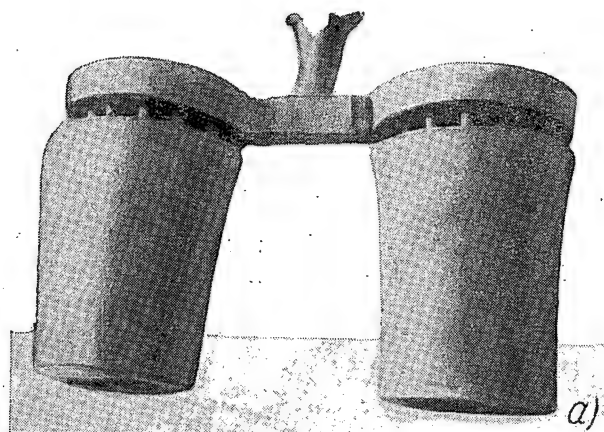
Схема заливки форм под заготовки из магниевого чугуна:
